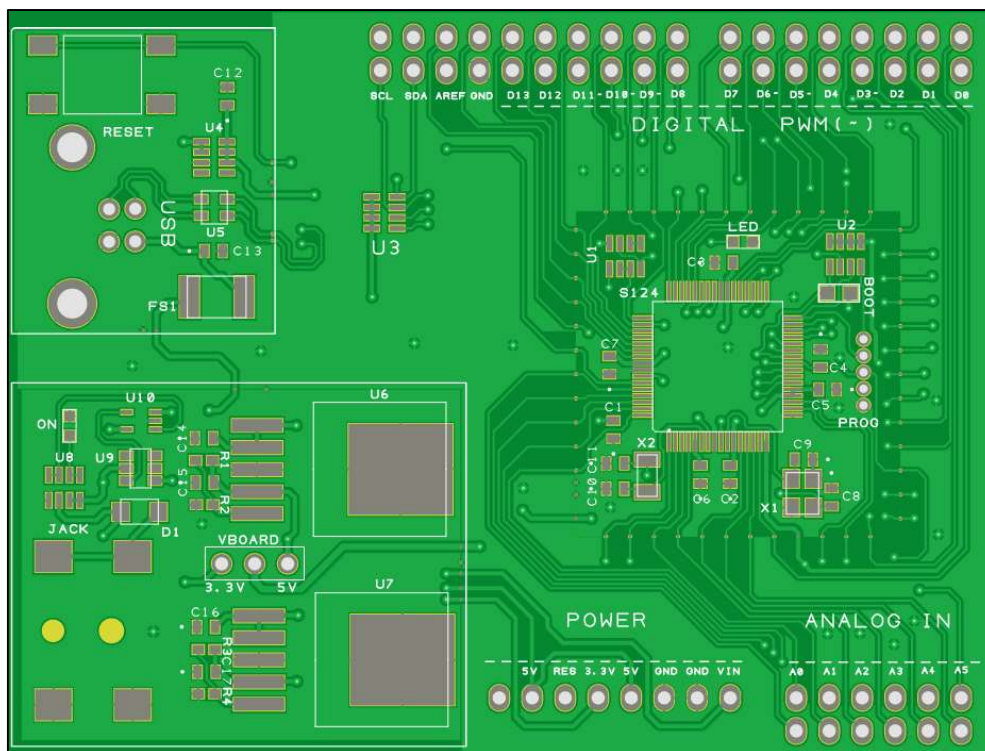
Vista previa del módulo PCB en PCB Visualizer: cara TOP
